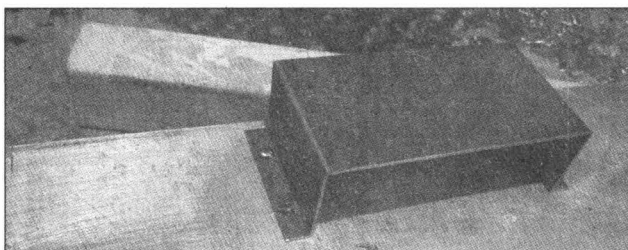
Изготовлен и установлен на свое место воздуховод для быстрого вывода горячего воздуха из корпуса
